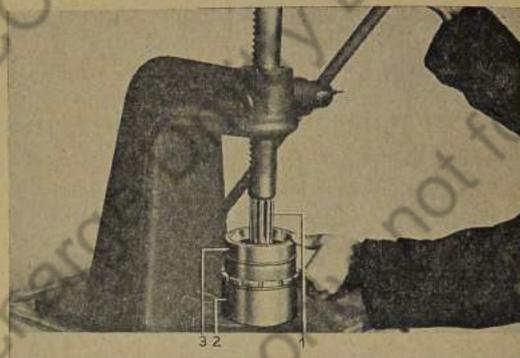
Flanschwelle aus Einstellbuchse herausdrücken
